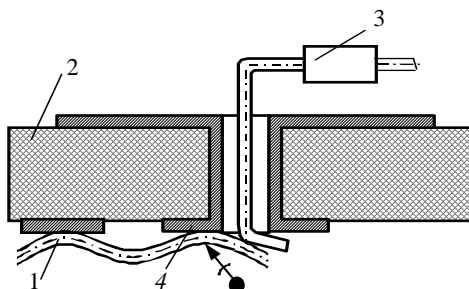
Схема проводного монтажа незакрепленными проводами
